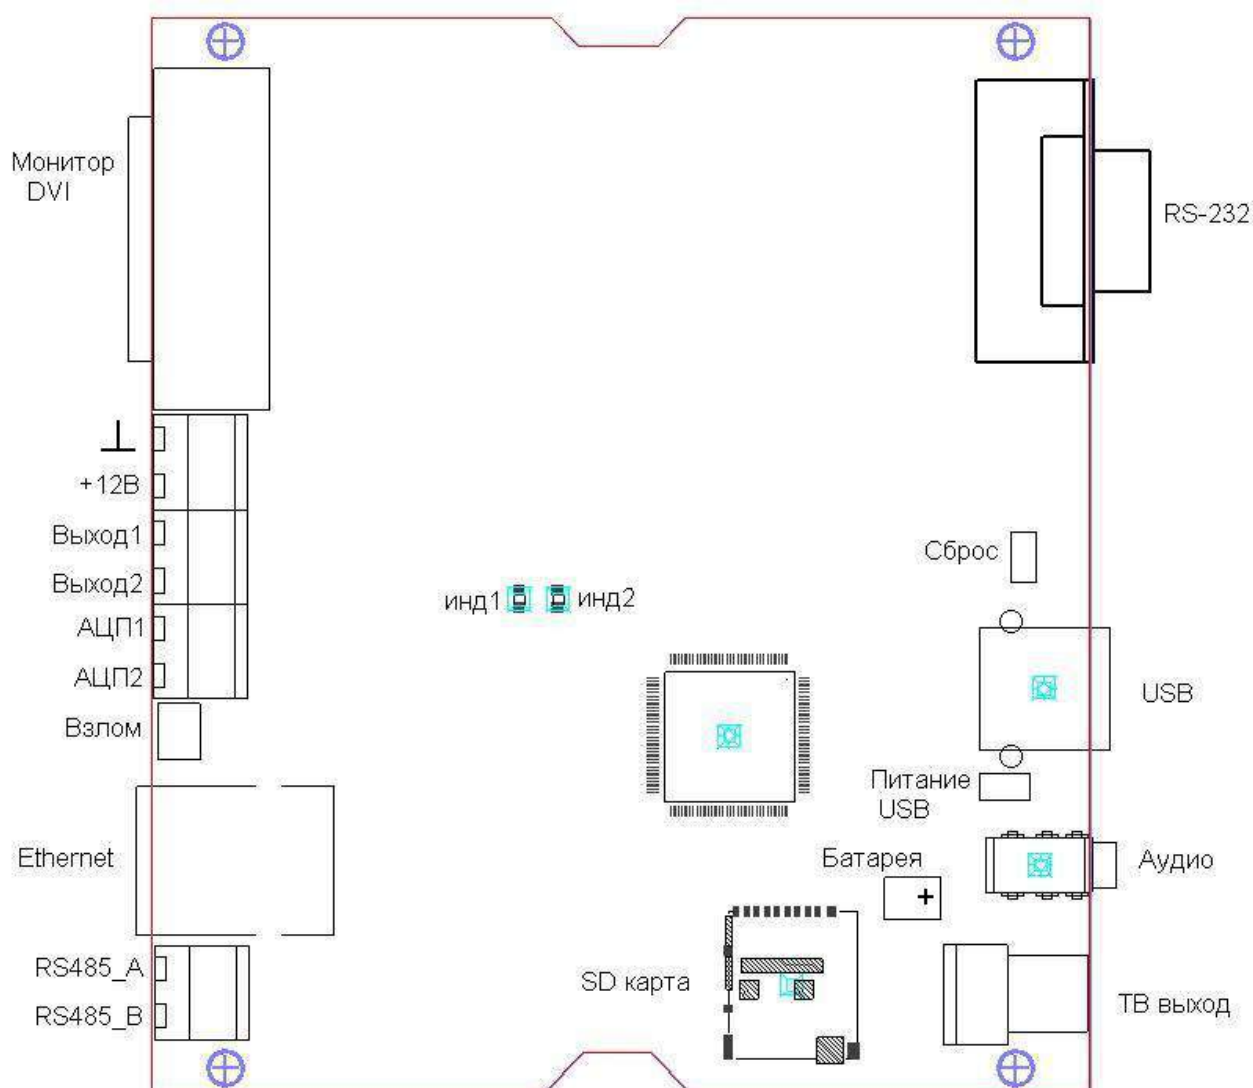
Общий вид платы коммуникатора TCP/IP-010
